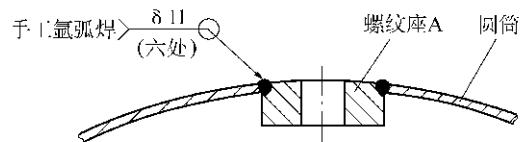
螺纹座 A 与圆筒的焊接示意图
